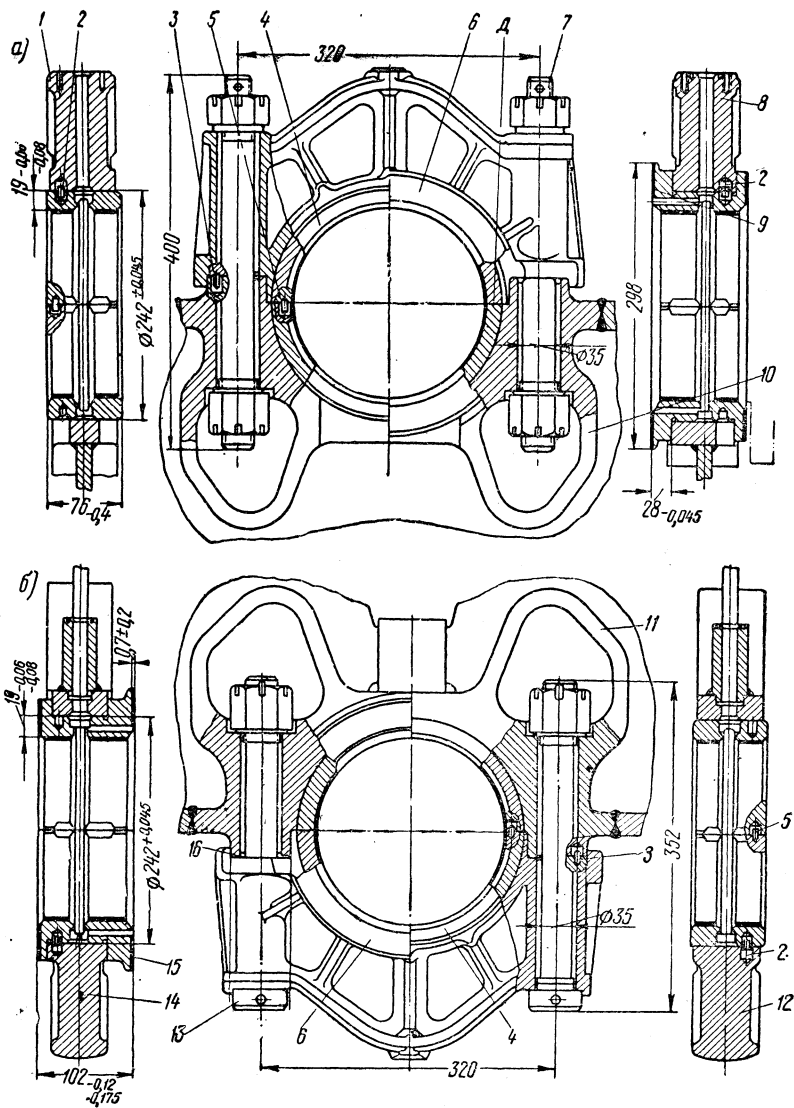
Коренные подшипники нижнего и верхнего коленчатых валов дизеля 2Д100:
